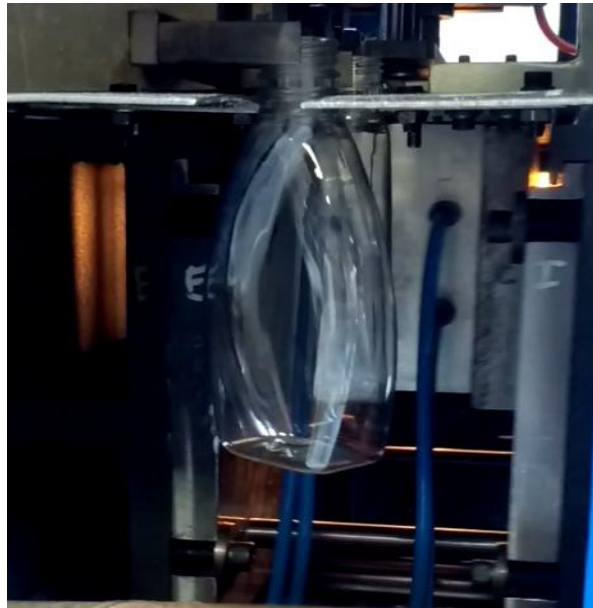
Cierre de Molde de 1o 2 Cavidades y soplado de la Preforma
